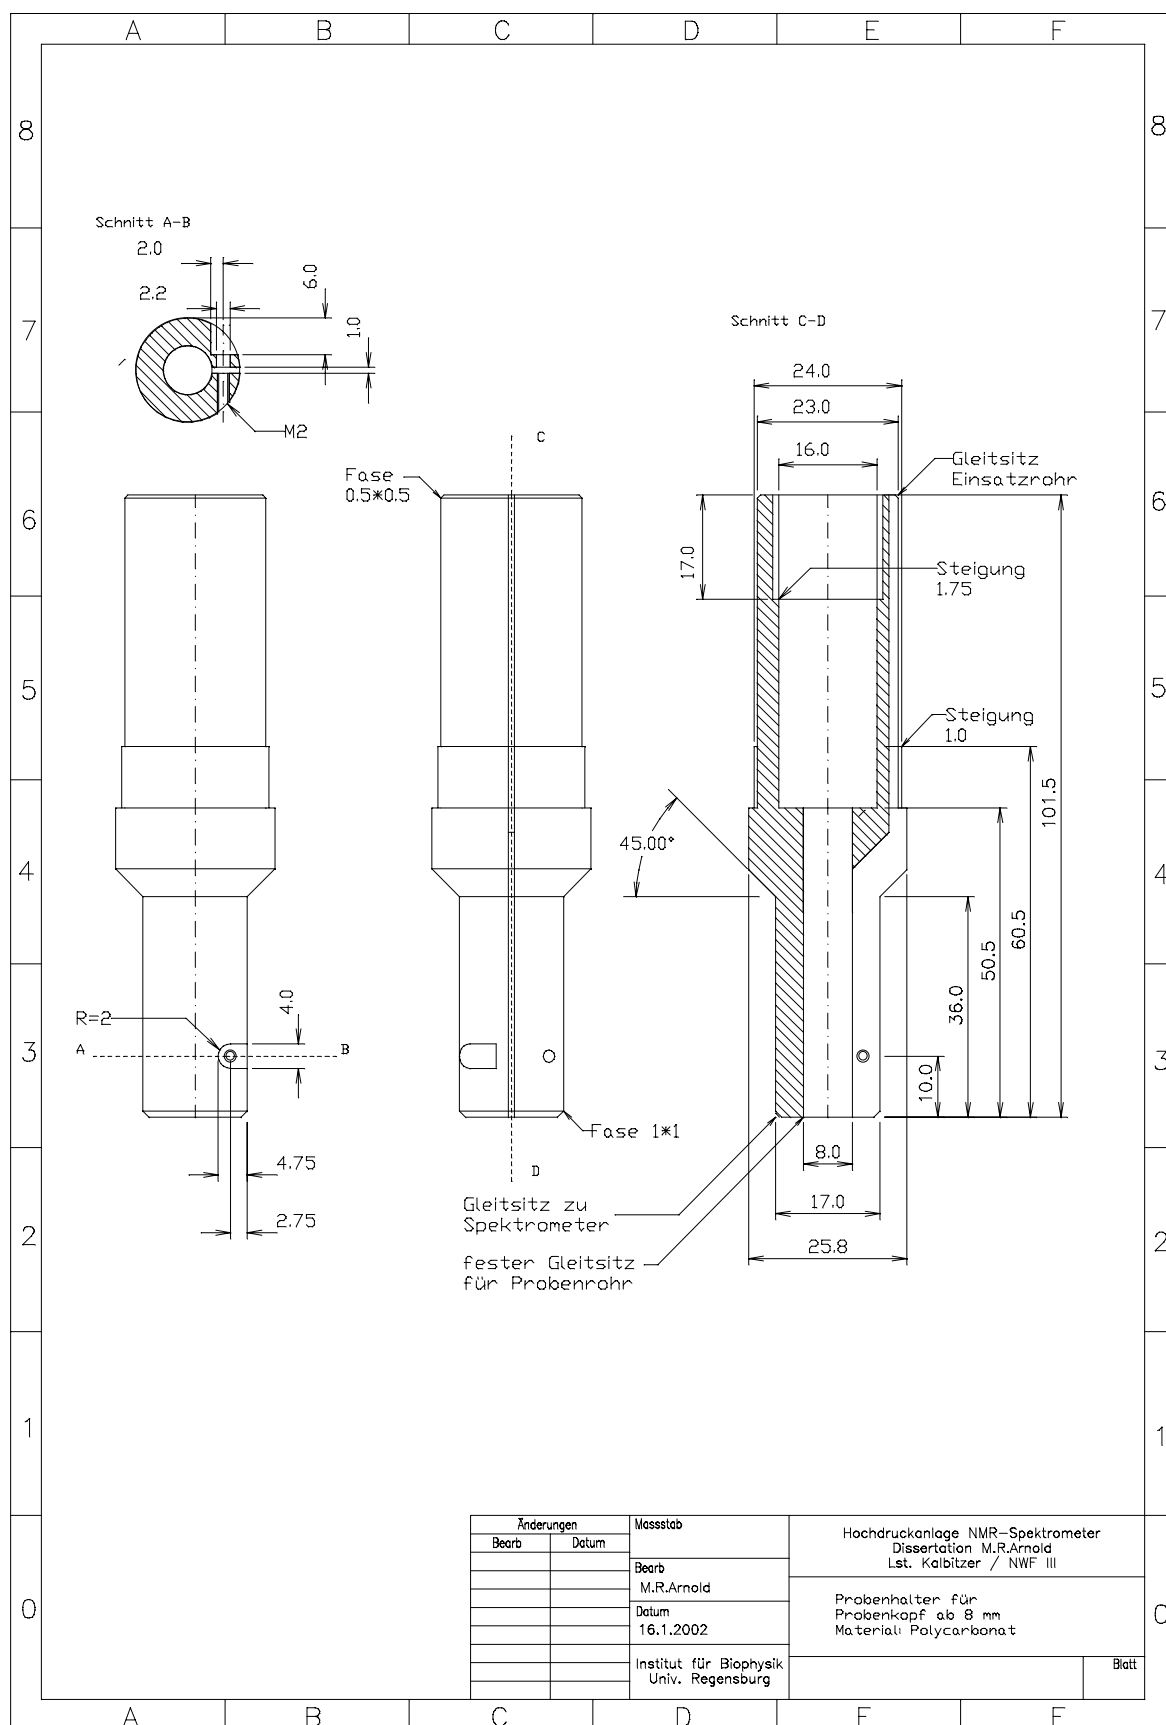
Halter für Probenrohre mit 8 mm Aussendurchmesser zur Verwendung mit beiden Hochdruckautoklaven. Das Probenrohr wird durch Festziehen einer Messingschraube wie in einer Spannzange festgeklemmt. Der Längsschlitz dient zum Einführen eines Thermoelements in den Messbereich.
